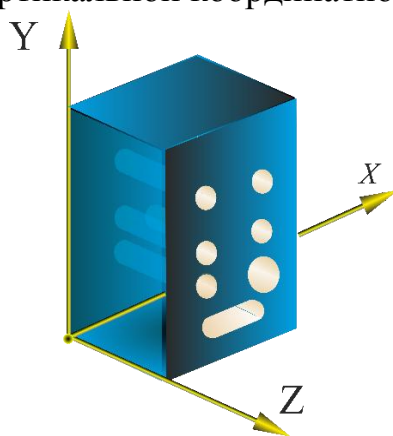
Эскиз детали с её положением и поверхностями обработки
